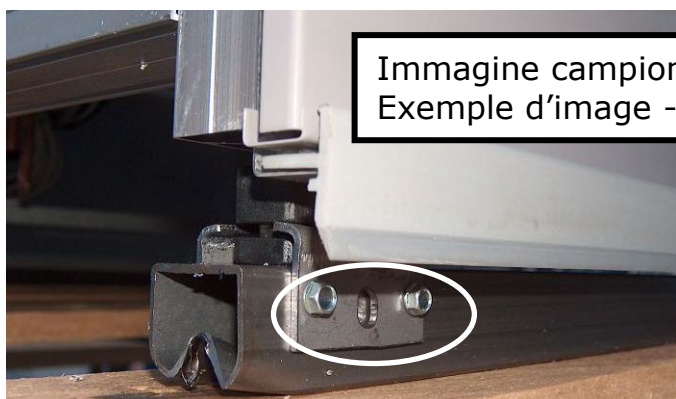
dettaglio viti bloccaggio clip / detail of clip fastening screws / Detailansicht: Befestigungsschrauben für Klammer
